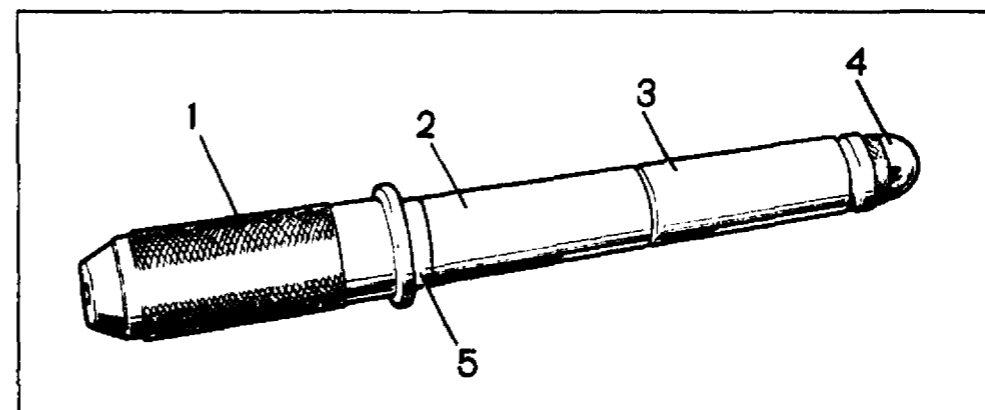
Установка поршневого пальца на приспособление А.60325 для запрессовки:
